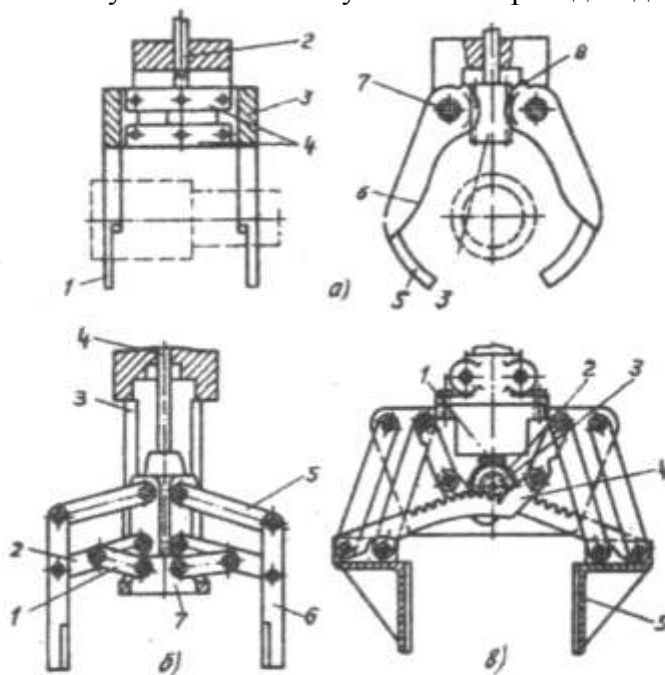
Центрирующие широкодиапазонные захватные устройства: а — с двумя поворотными губками; б и в — с параллельным перемещением губок
